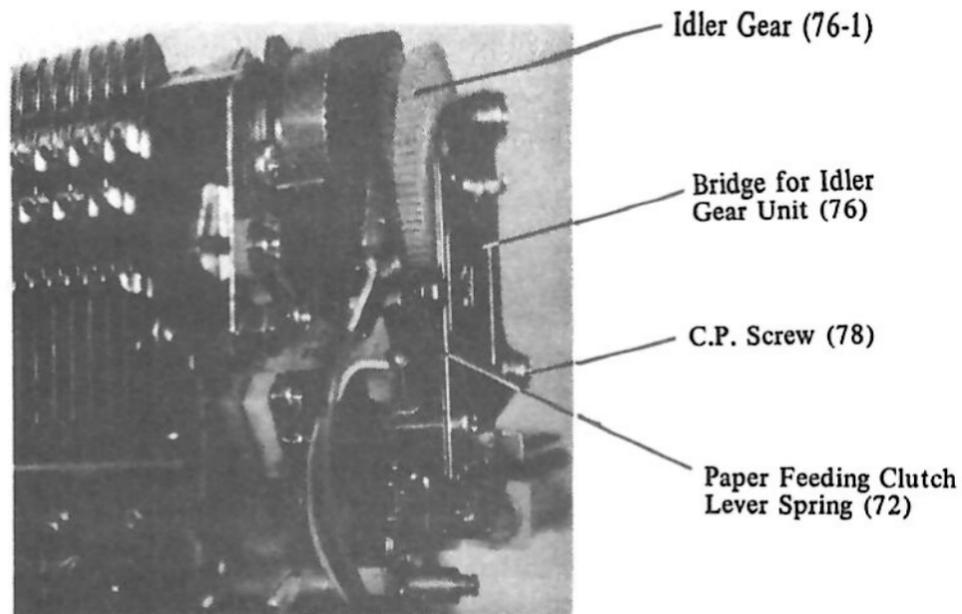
Ausbau der Brücke vom Zwischenrad
